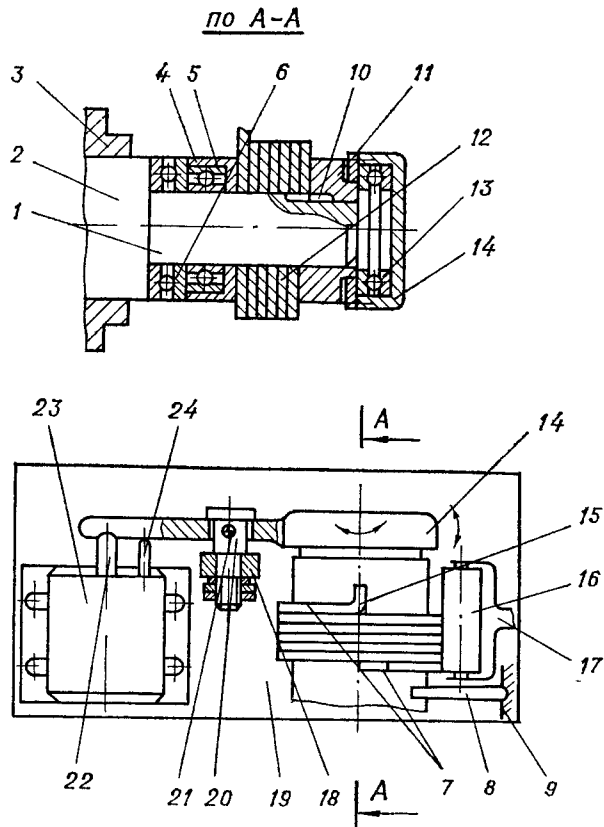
Схема приспособления для непрерывной навивки спиралей шнеков
